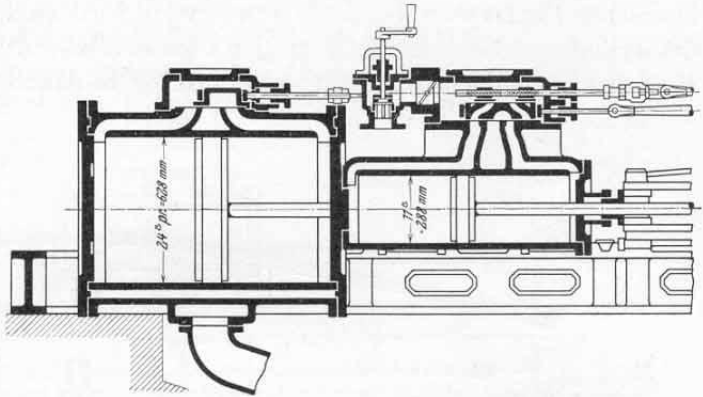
Woolfsche Maschine von Wöhlert-Berlin um 1860.
